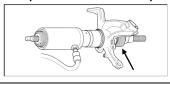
KL-0039-1002 - Aufnahmeadapter für Spannmutter und Druckspindel
